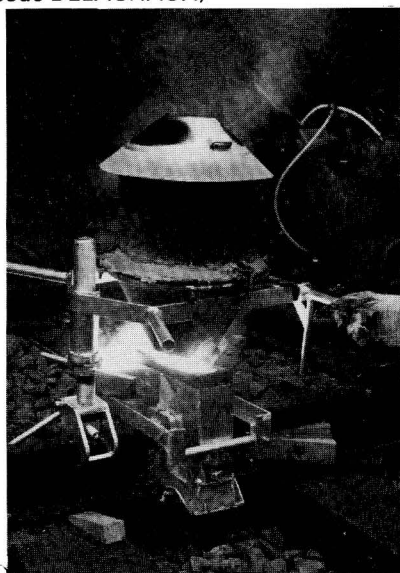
Coulée d'une soudure ALUMINOTHERMIQUE
